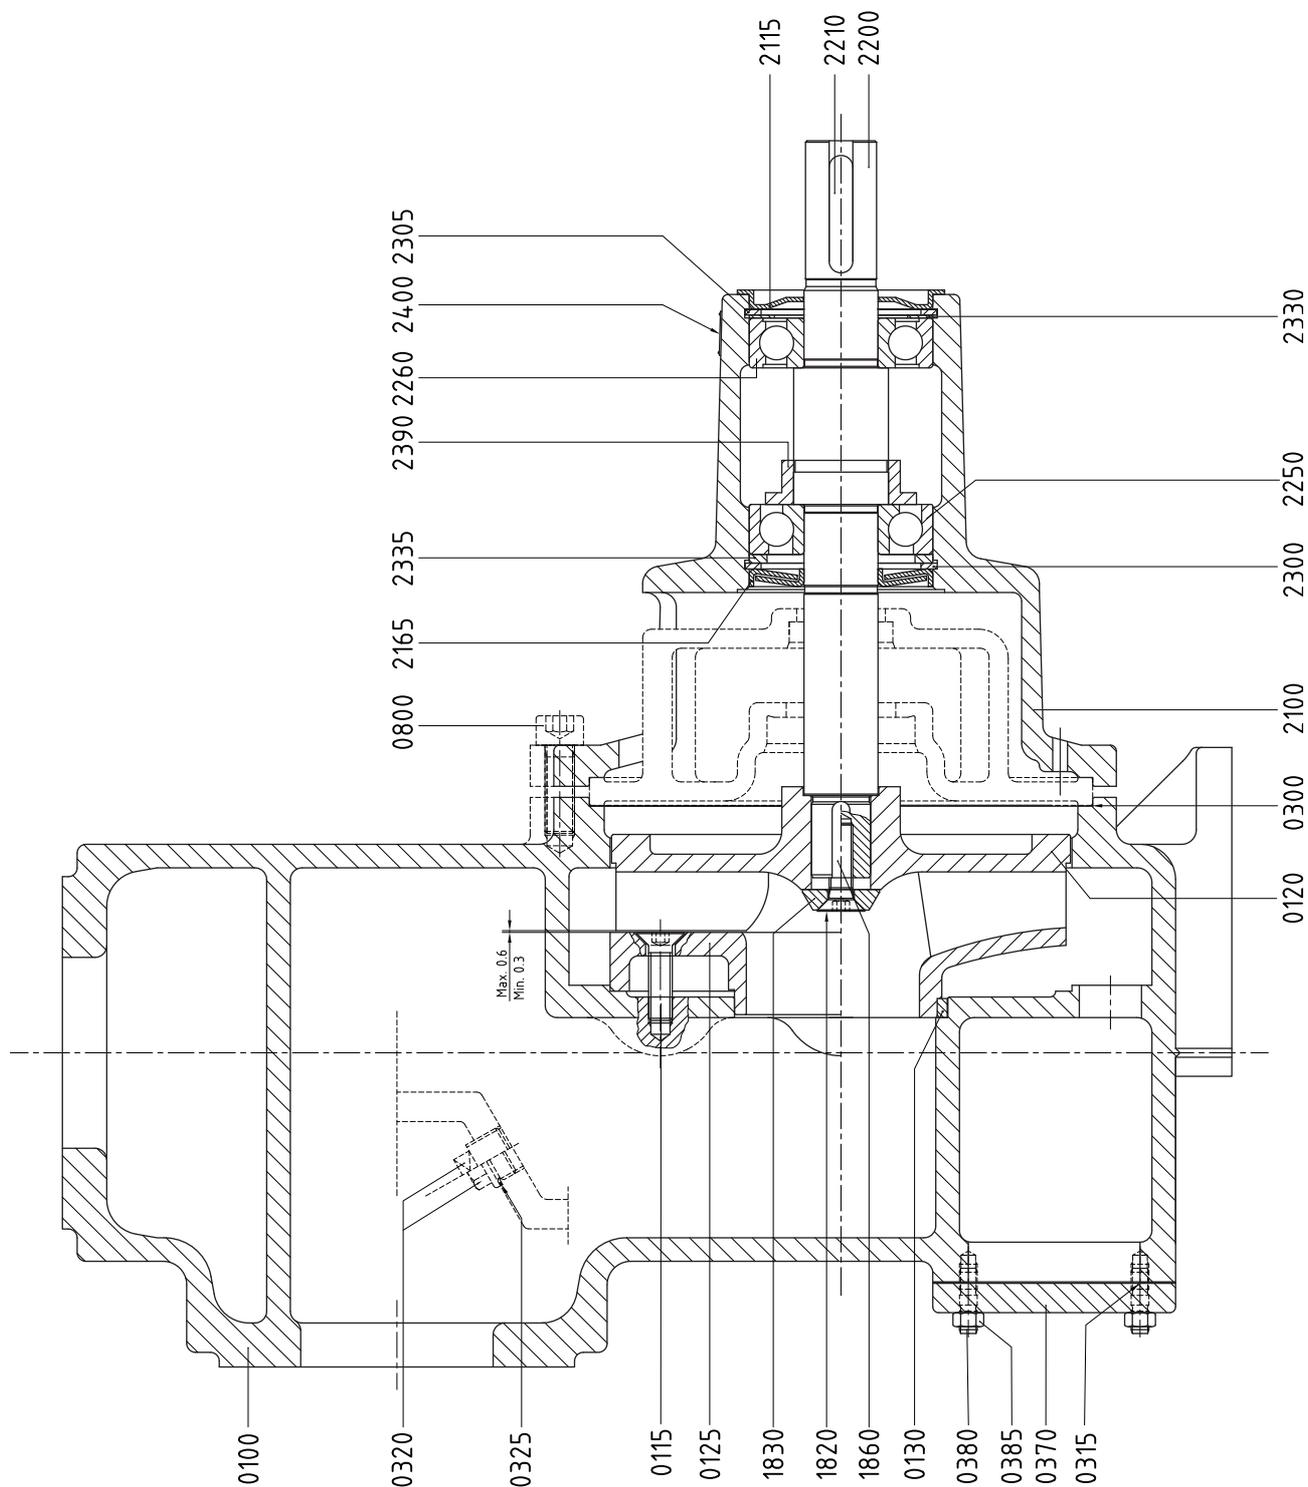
Plano seccional FRE - soporte del cojinete 2.
